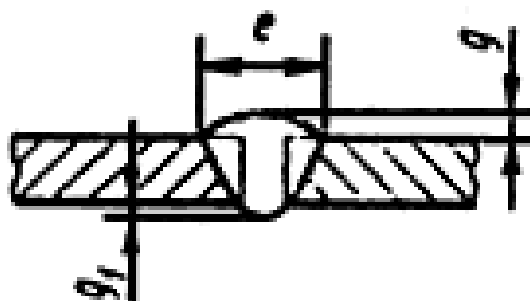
Конструктивные элементы сварочного шва, согласно ГОСТ 14771-76.
